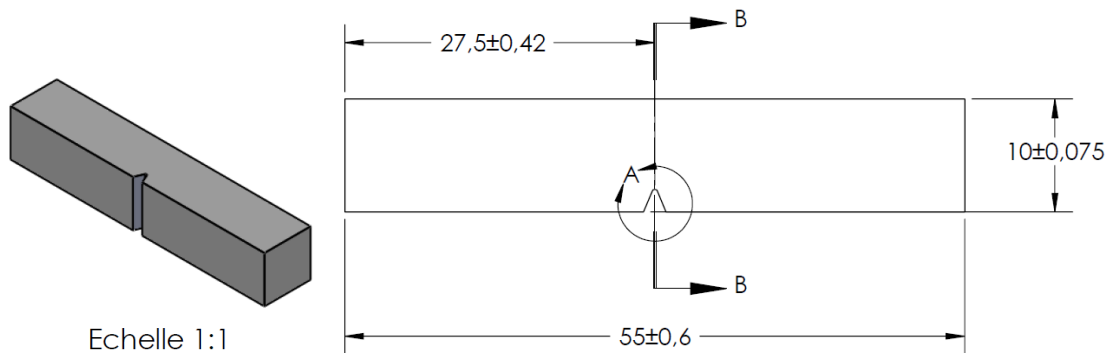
Géométrie utilisée pour les éprouvettes de Charpy.
